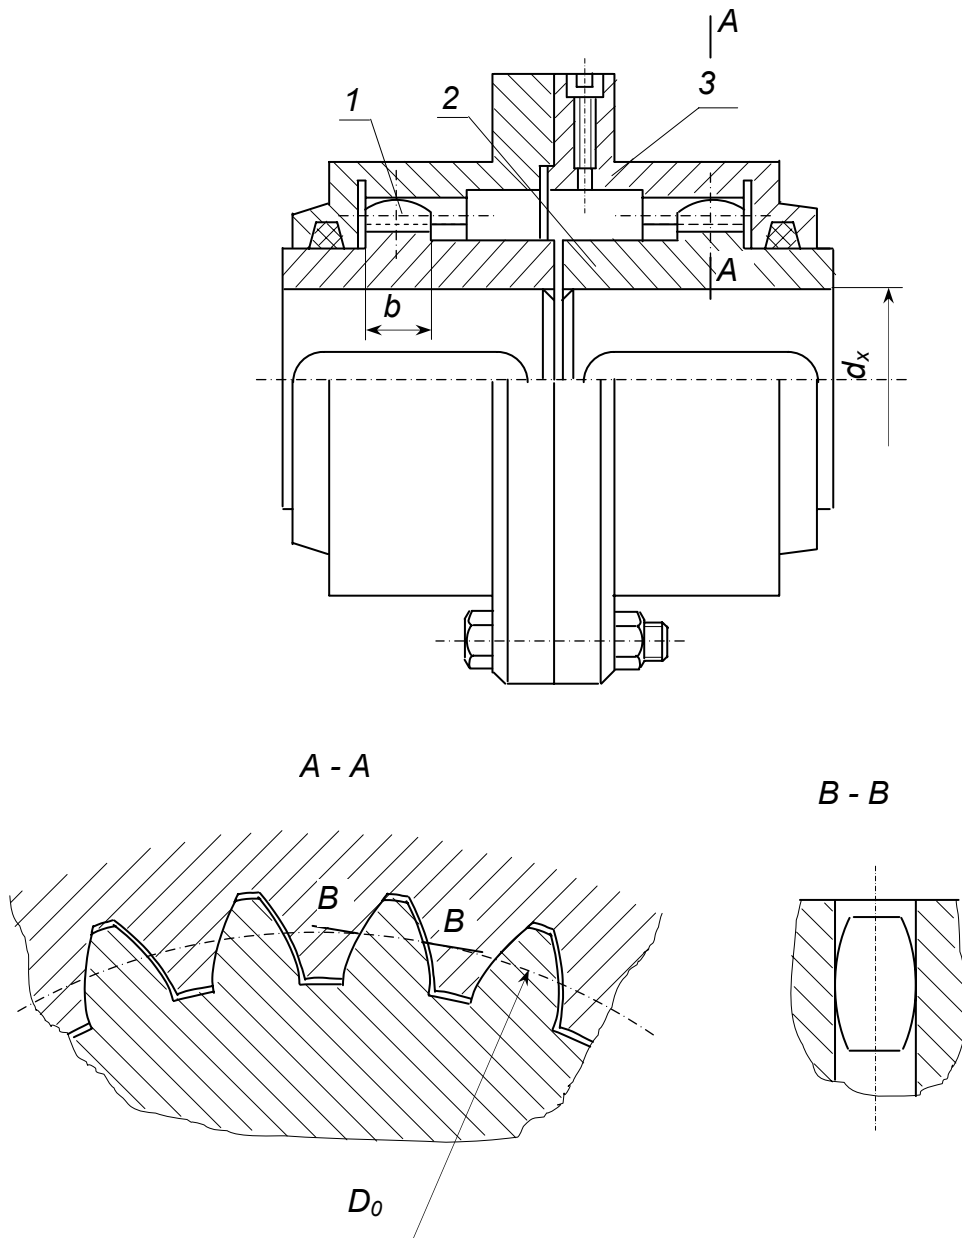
Конструкція зубчастої муфти: 1, 2 – втулки з зовнішніми зубцями; 3 – складова обойма з внутрішніми зубцями
